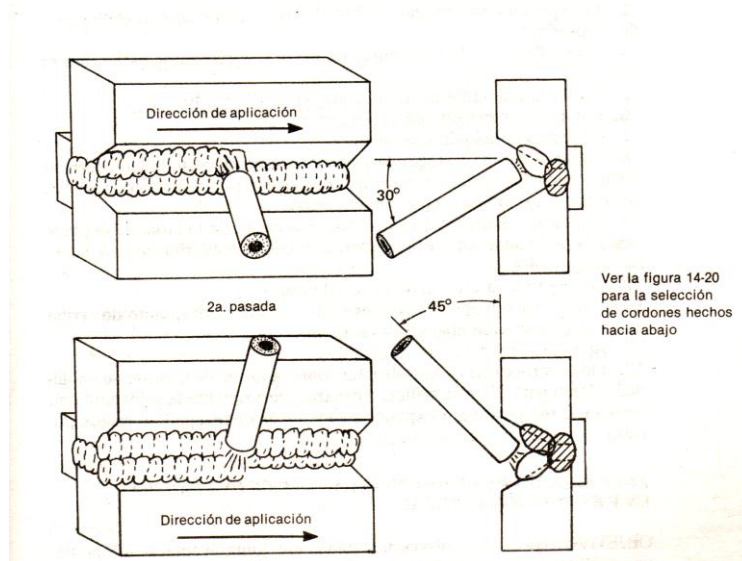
Realización del 2º y 3º cordón de soldadura.
